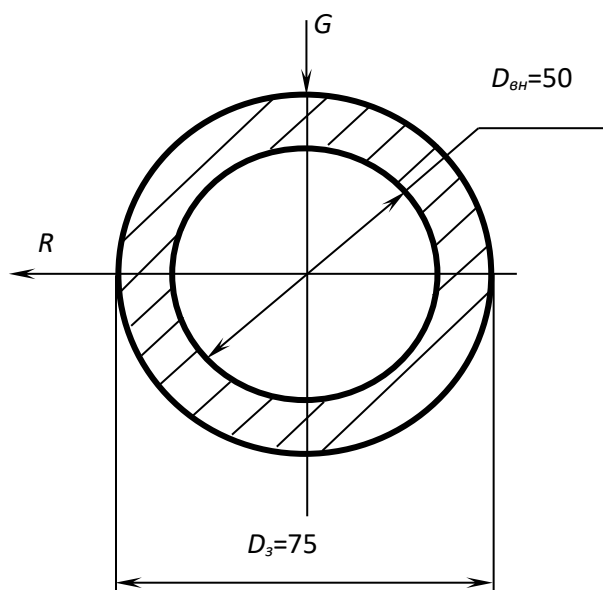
Схема сил, які діють в перерізі вала
